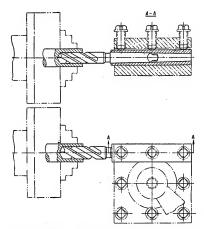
Установка сверла в специальной втулке, укрепленной в резцедержателе токарного станка.
